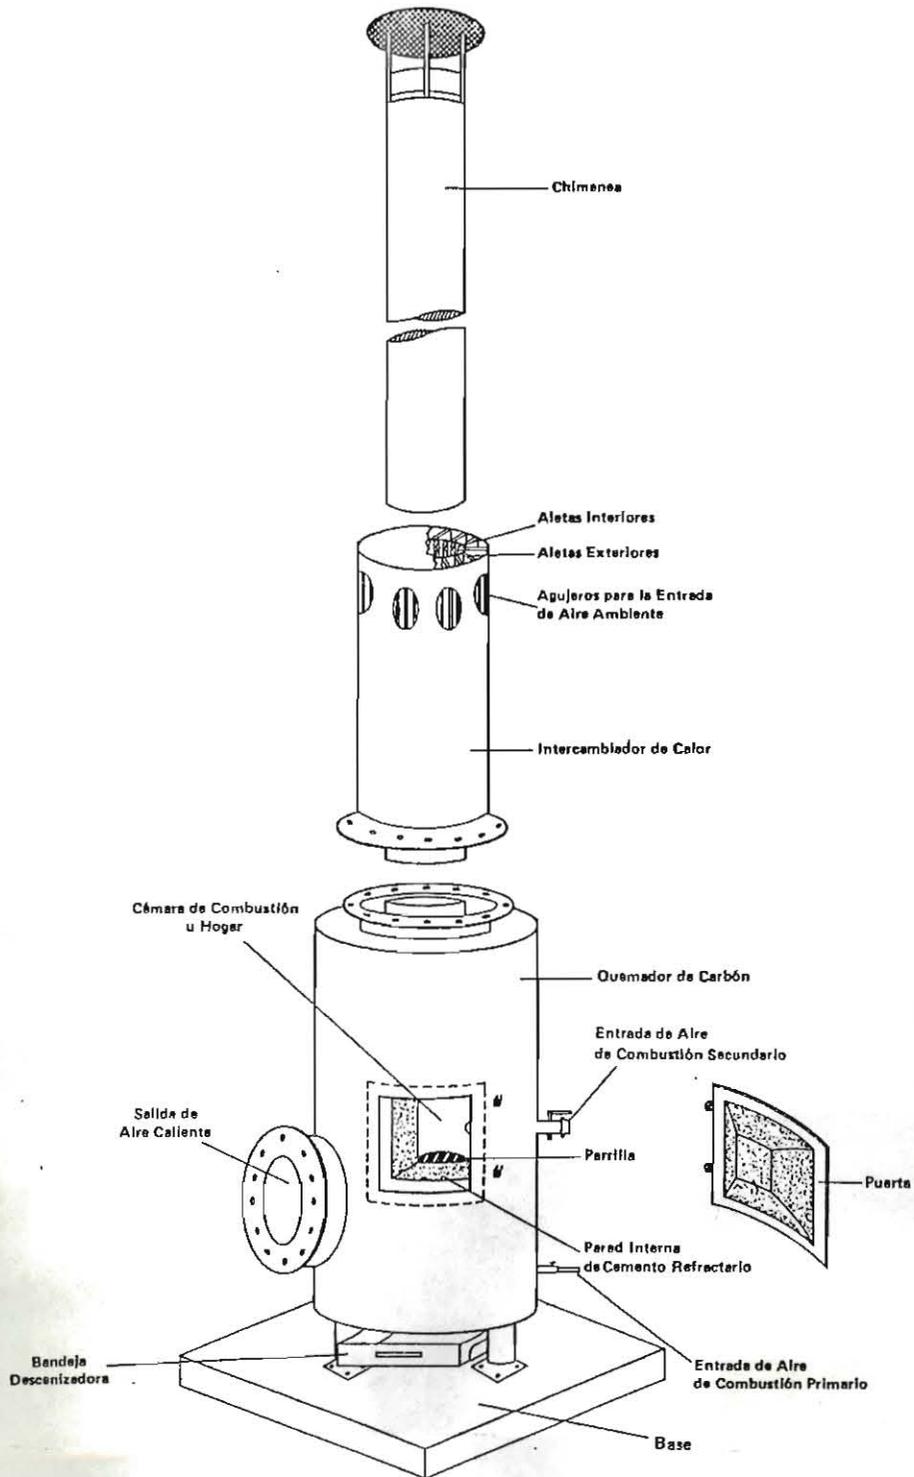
Conjunto quemador de carbón e intercambiador de calor.
